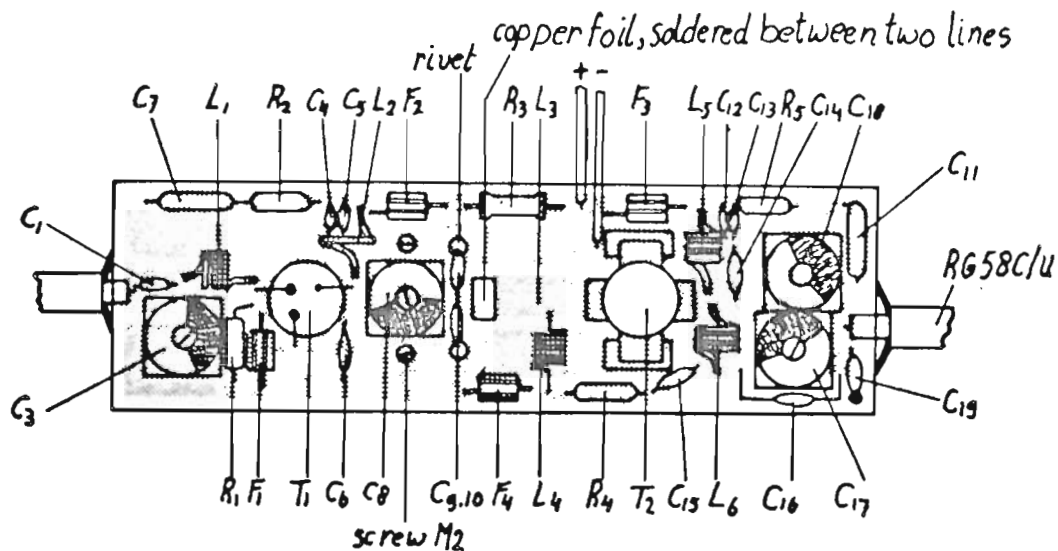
Circuito stampato visto dalla parte dei componenti
